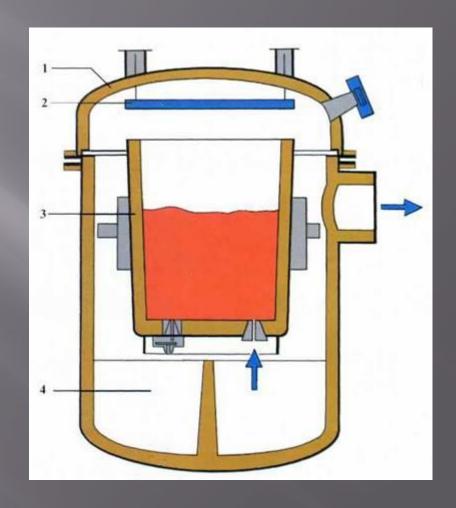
Установка для вакуумной обработки металла в ковше
